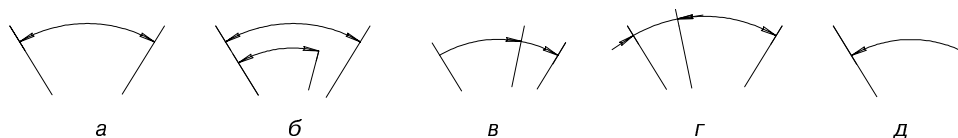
Типы угловых размеров: а — обычный угловой; б — от общей базы; в — цепной; г — с общей размерной линией; д — с обрывом
